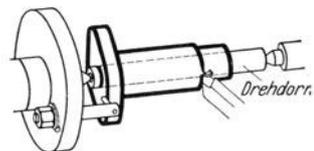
Aufnahme eines Werkstückes auf gewöhnlichem Drehdorn.
